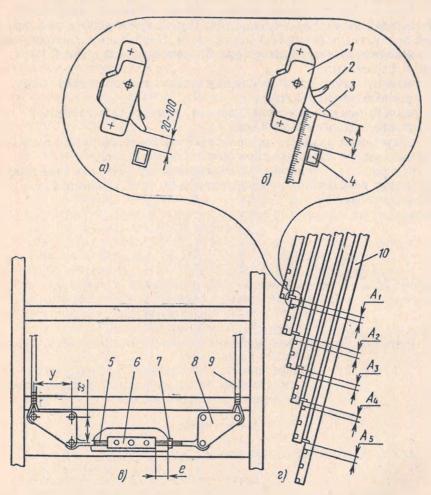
Регулировка канатов автолестницы АЛ-45(257), ПМ-109: I — замыкатель; 2 — отбрасыватель; 3 — упор; 4 — ступень; 5 — стяжка; 6 — муфта; 7 — гайка; 8 — качалка; 9 — канат; 10 — комплект колен
